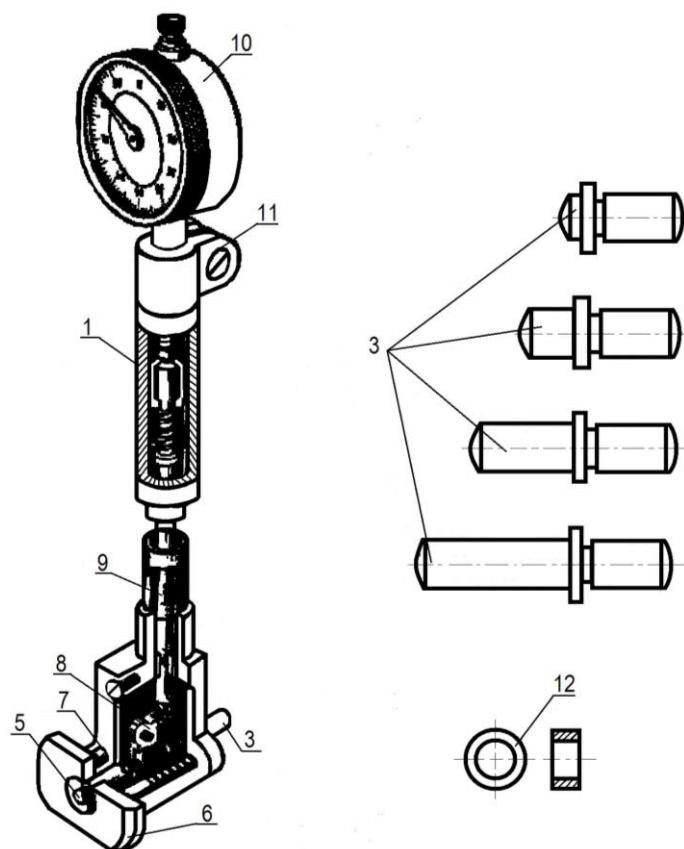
Индикаторный нутромер со сменными гладкими измерительными вставками
